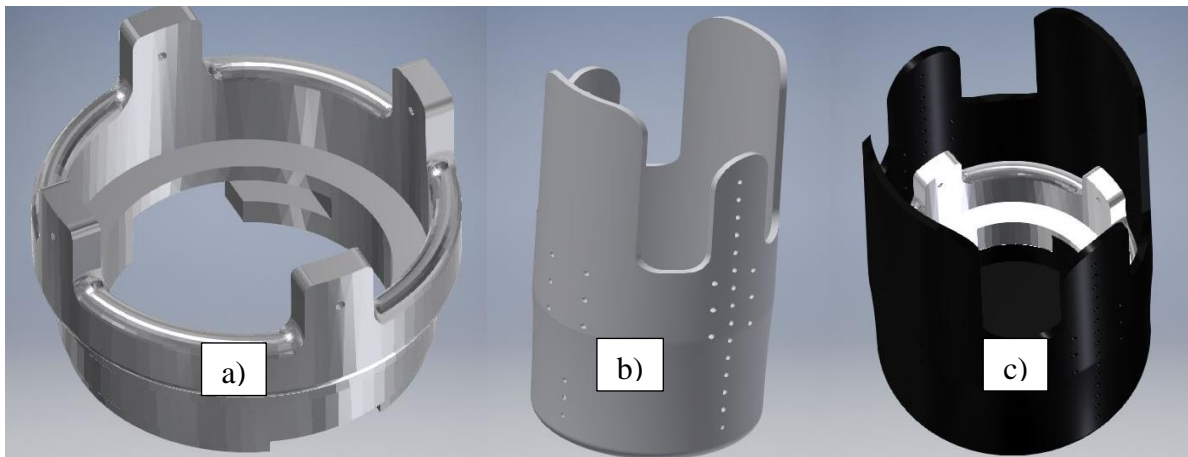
socket y ensamble: a) acople – b) socket – c) ensamble de acople y socket
